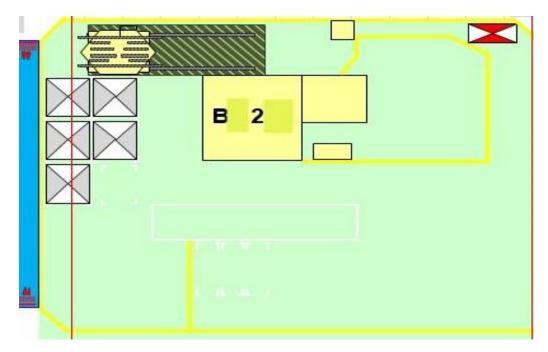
Layout Prensa Blankin 200 (Actual)
